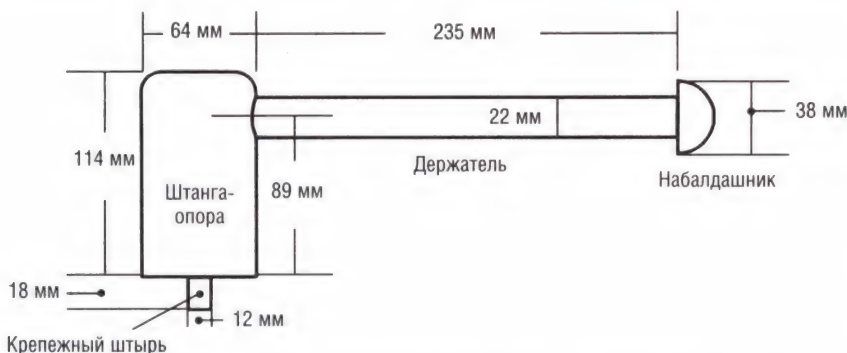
Вид сбоку держателя на штанге-опоре и их размеры.
